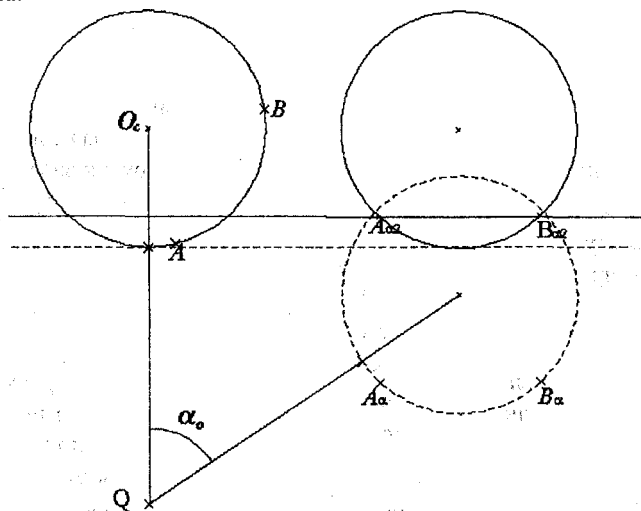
Схема вступления в контакт с заготовкой участка AB бруска
